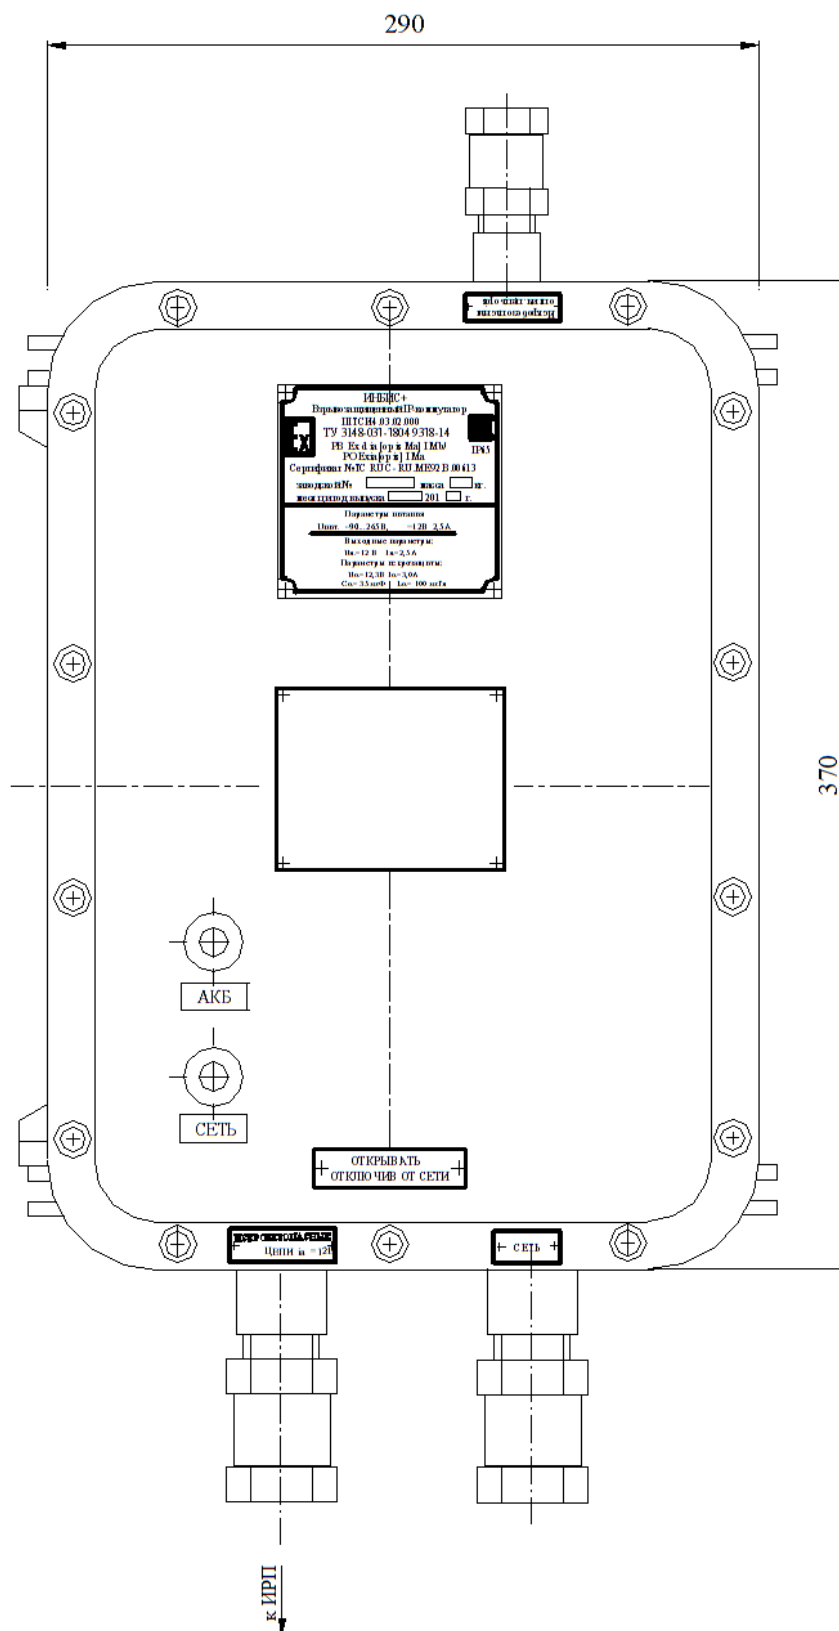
Чертёж корпуса IP-коммутатора.
